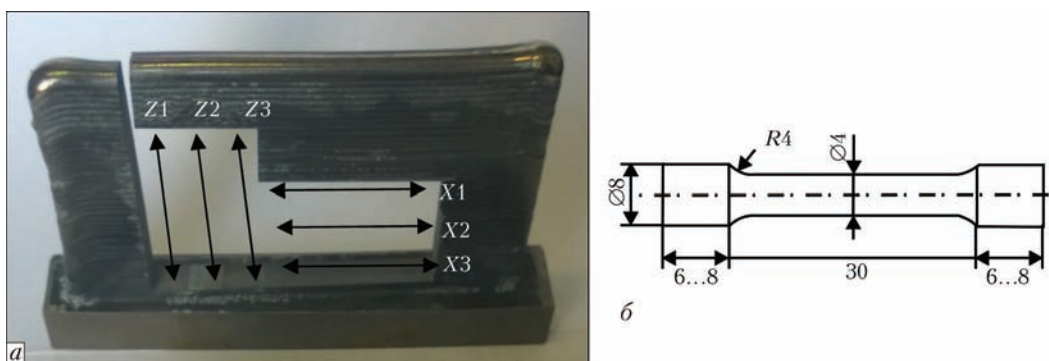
Схема вырезки образцов для механических испытаний (*а*), чертеж образца (*б*)
